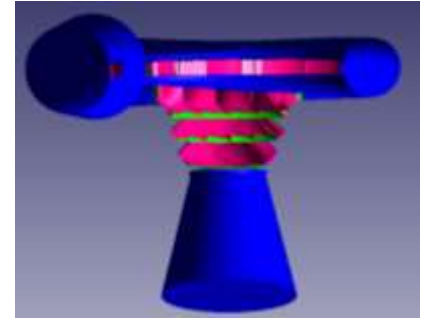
Трехмерная модель РОД400 гидроагрегата
